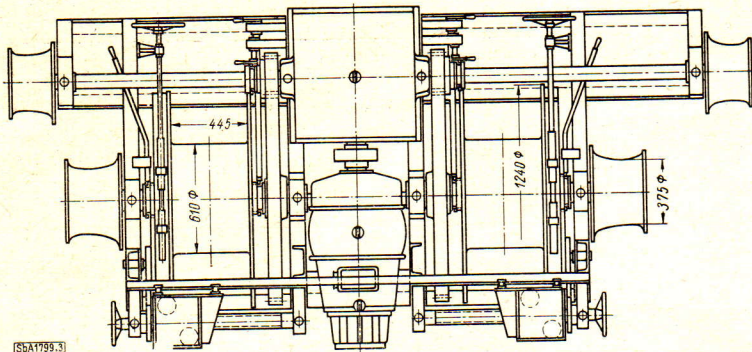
2,5-t-Fischnetzwinde für „Seiner“, Draufsicht
